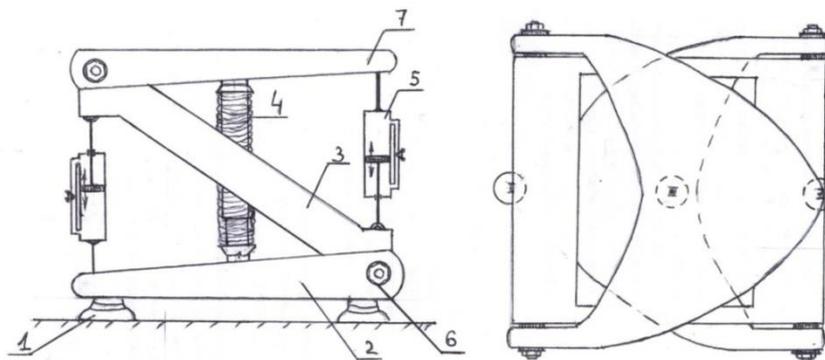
Рычажная подвеска сидения с пневмоцилиндрами
